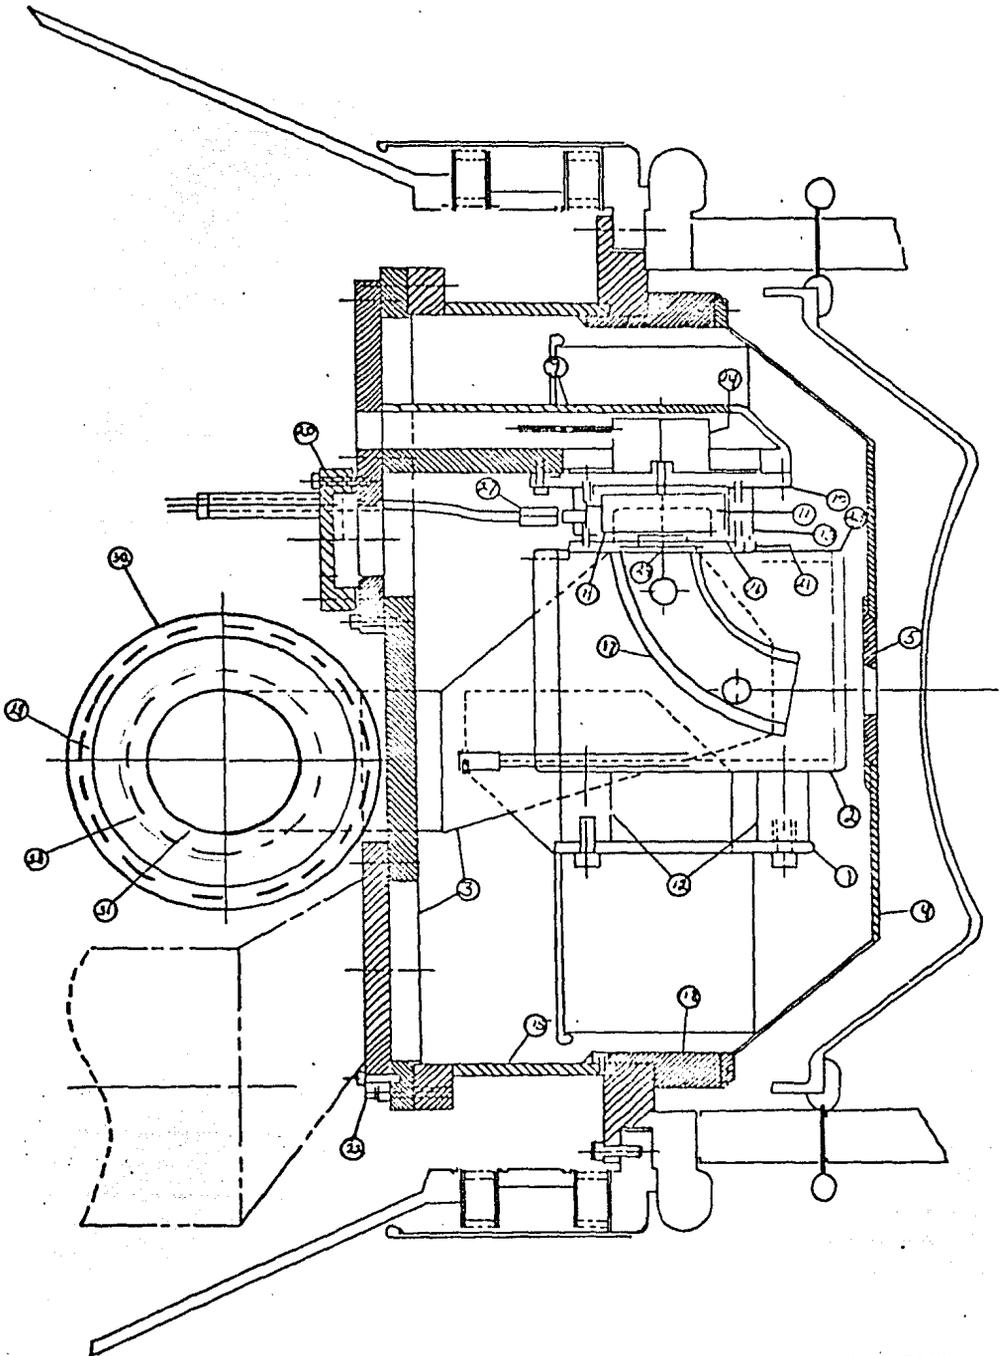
COMPONENTES MECANICAS DE UNA FUENTE DE IONES MAGNETRON.
